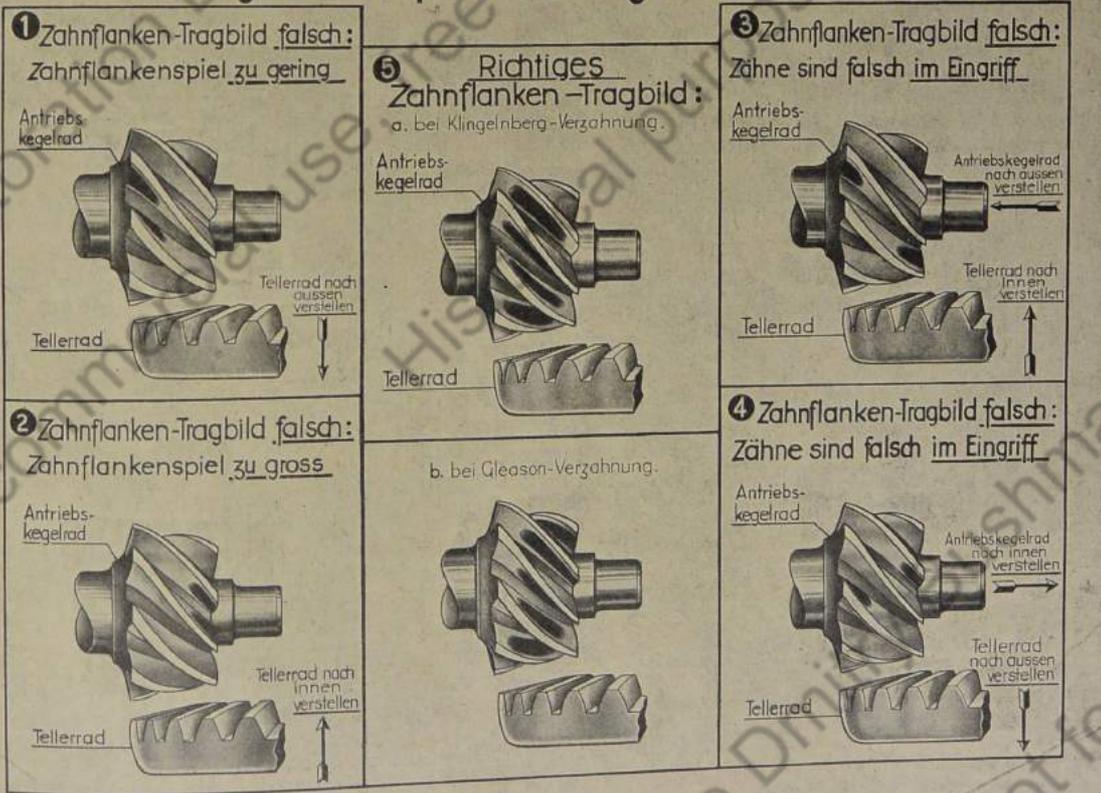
Richtiges Zahnflanken-Tragbild ermitteln
